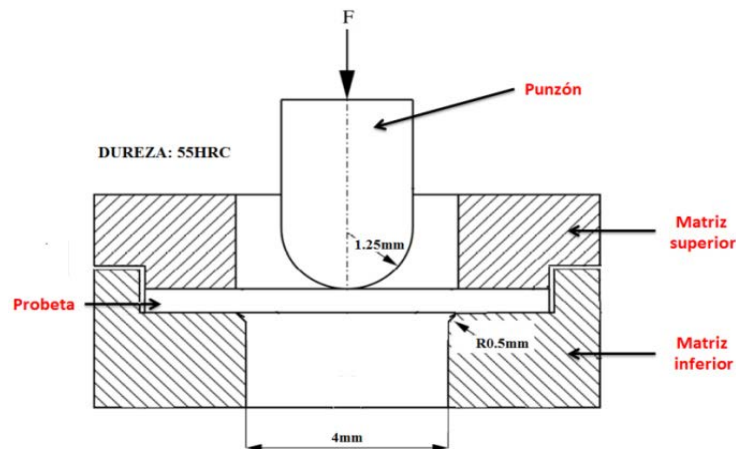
Dimensiones del utillaje y la probeta a ensayar.
